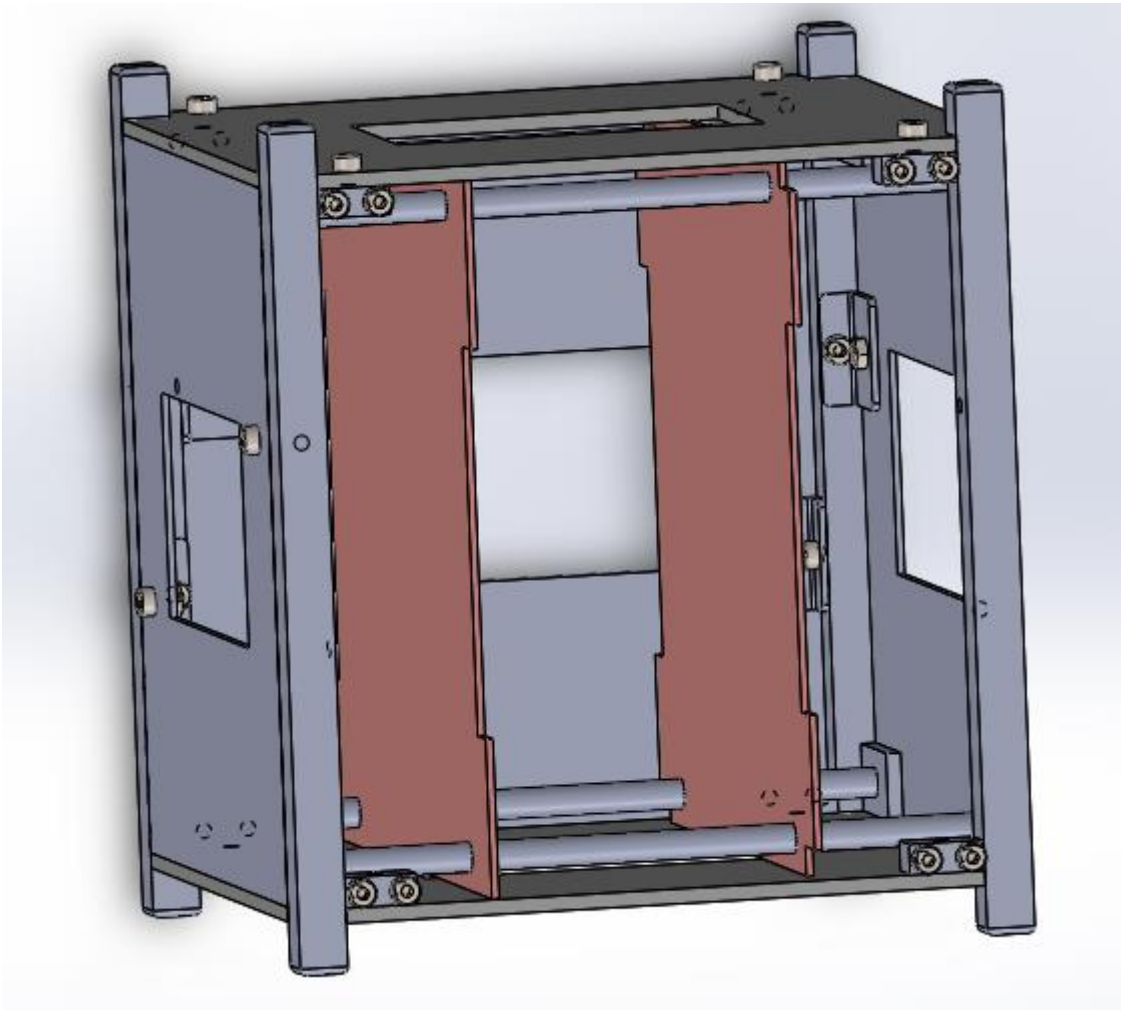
Estrutura com detalhe das peças de fixação (*brackets, spacers e boss*)
